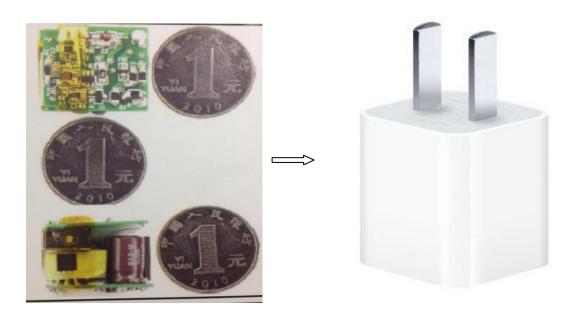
整体设计的 PCB 面积均如硬币大小,可以让外观做到迷你型。
